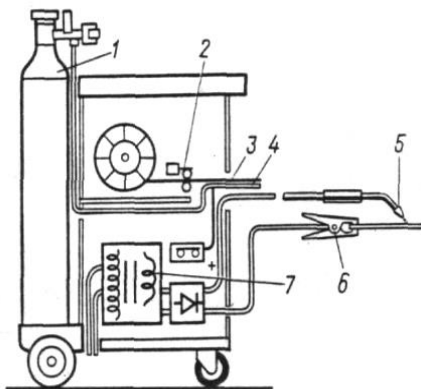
Схема полуавтомата для сварки в среде защитных газов: 1 - баллон с углекислотой; 2 - механизм подачи проволоки; 3 - проволока; 4 - трубопровод подачи газа; 5 - горелка; 6 - заземление; 7 - трансформатор
